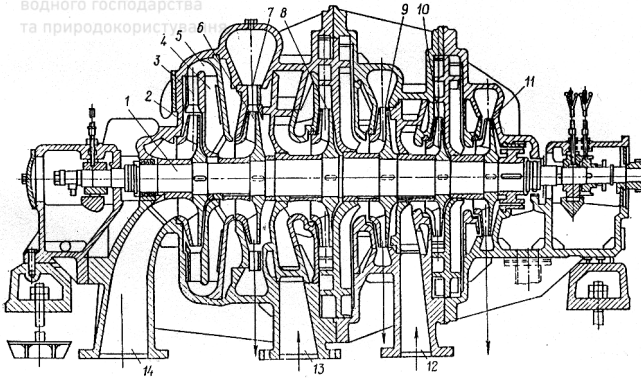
Відцентровий шестиступінчастий компресор: 1- вал; 2, 6, 8, 9, 10, 11- робочі колеса; 7-кільцеві дифузори; 4-зворотний напрямний апарат; 5- напрямний апарат; 12, 13- канали для підводу газу з холодильників; 14- всмоктувальний патрубок
